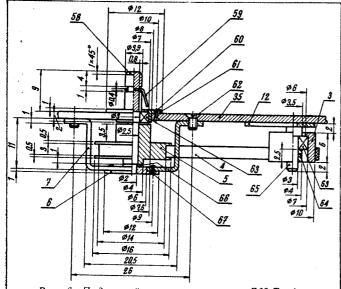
Подающий узел: 3 — ролик, Л62-Т; 4 — пассик; 5 — шкив, Д16-Т; 6 — втулка, Бр. Б2; 7 кронштейн, Л62; 12 — рычаг обратной перемотки, Ст.20; 35 — шасси ЛПМ; 58 — валик. Ст.2X13, запрессовать в дет. 5; 59 — фиксатор, проволока запрессовать в дет. 3, 39 — фиксатор, проволька стальная класса $11 \varnothing 0.4$ мм, запрессовать в дет. 58; 60 — заклепка $\varnothing 1$ мм, 2 шт.; 61 — втулка, C т.45; 62 — винт $M2 \times 4$, 2 шт.; 63 — подшипник шариковый 2000083 ($7 \times 3 \times 2.5$ мм); 64 — кольцо, J 62-T, напрессовать на дет. 65; 65 — ось. Ст.2X13; 66 — шайба, текстолит толщиной 0,5 мм; 67 — заклепка \varnothing 1 мм, 2 шт.
